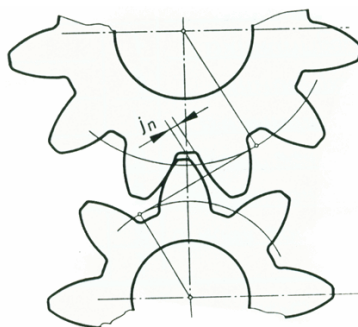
Боковой зазор в зубчатом зацеплении
